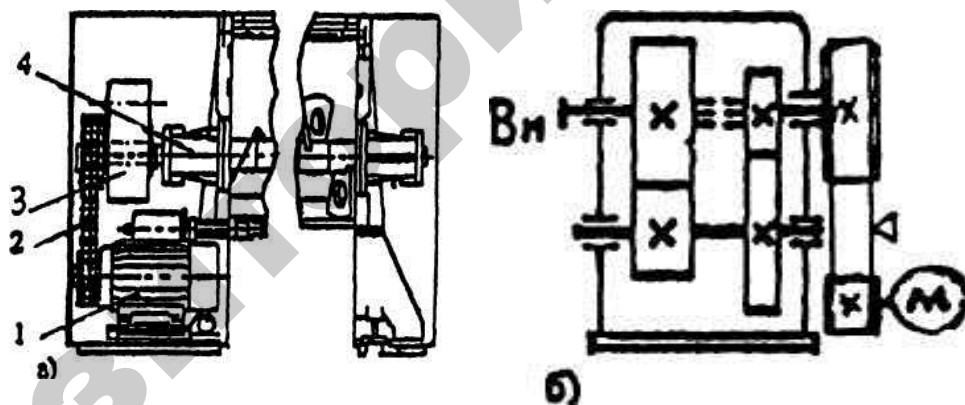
Привод смесителя кормов: 1 — электродвигатель, 2 — клиноременная передача; 3 — двухступенчатый соосный; 4 — ведущий вал смесителя; а) — общий вид привода; б) — кинематическая схема редуктора
